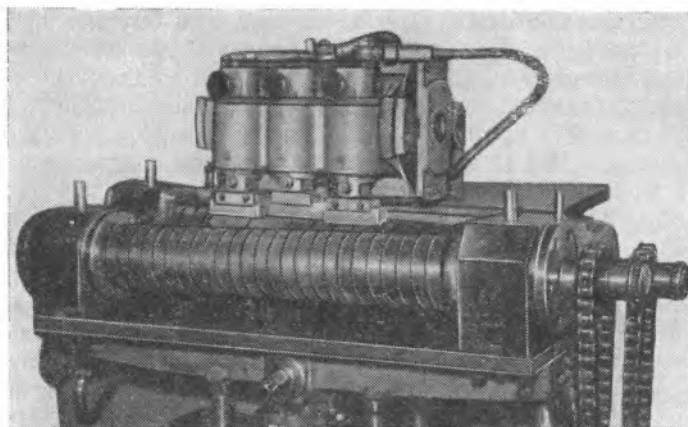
Трехшпindelный бесцентровой станок для суперфиниширования
